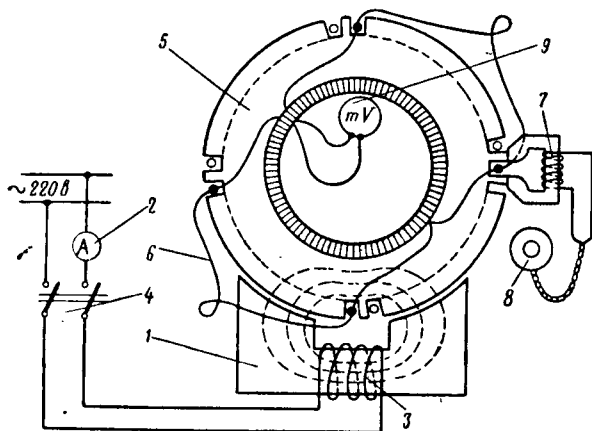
Принципиальная схема установки для проверки на витковое замыкание обмотки якоря:
